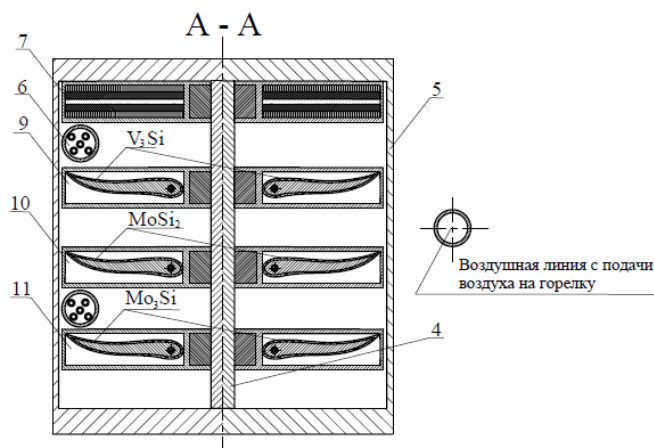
Схема врезки воздушных форсунок в корпус дожигателя
